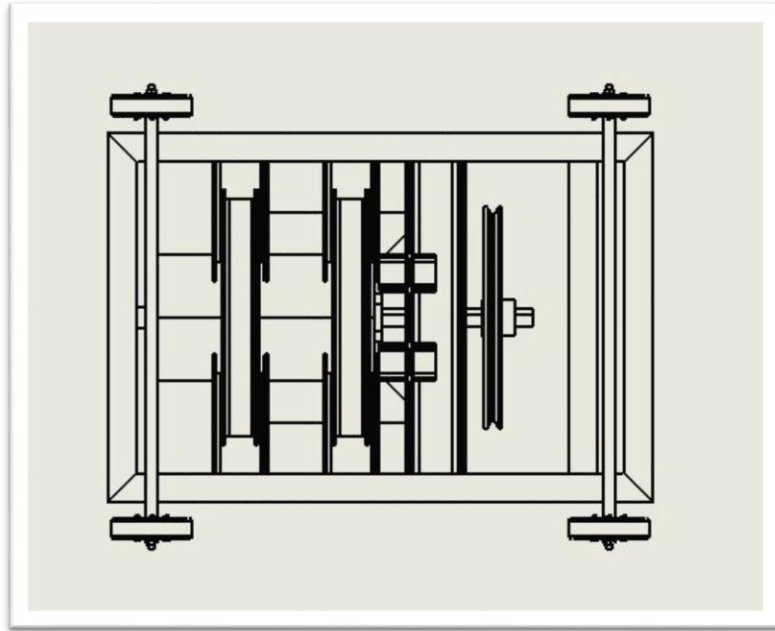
Tampak Samping Sketsa Mesin Briket
